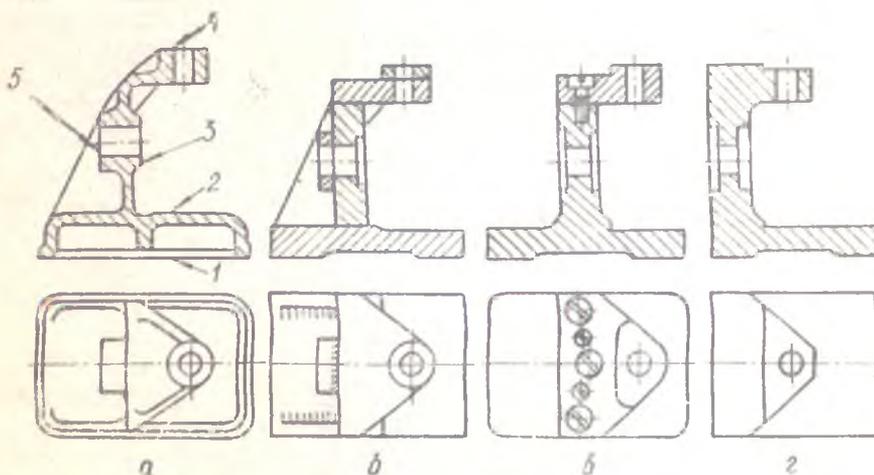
Варианты конструкции корпуса кондуктора при изготовлении его из различных видов заготовок
